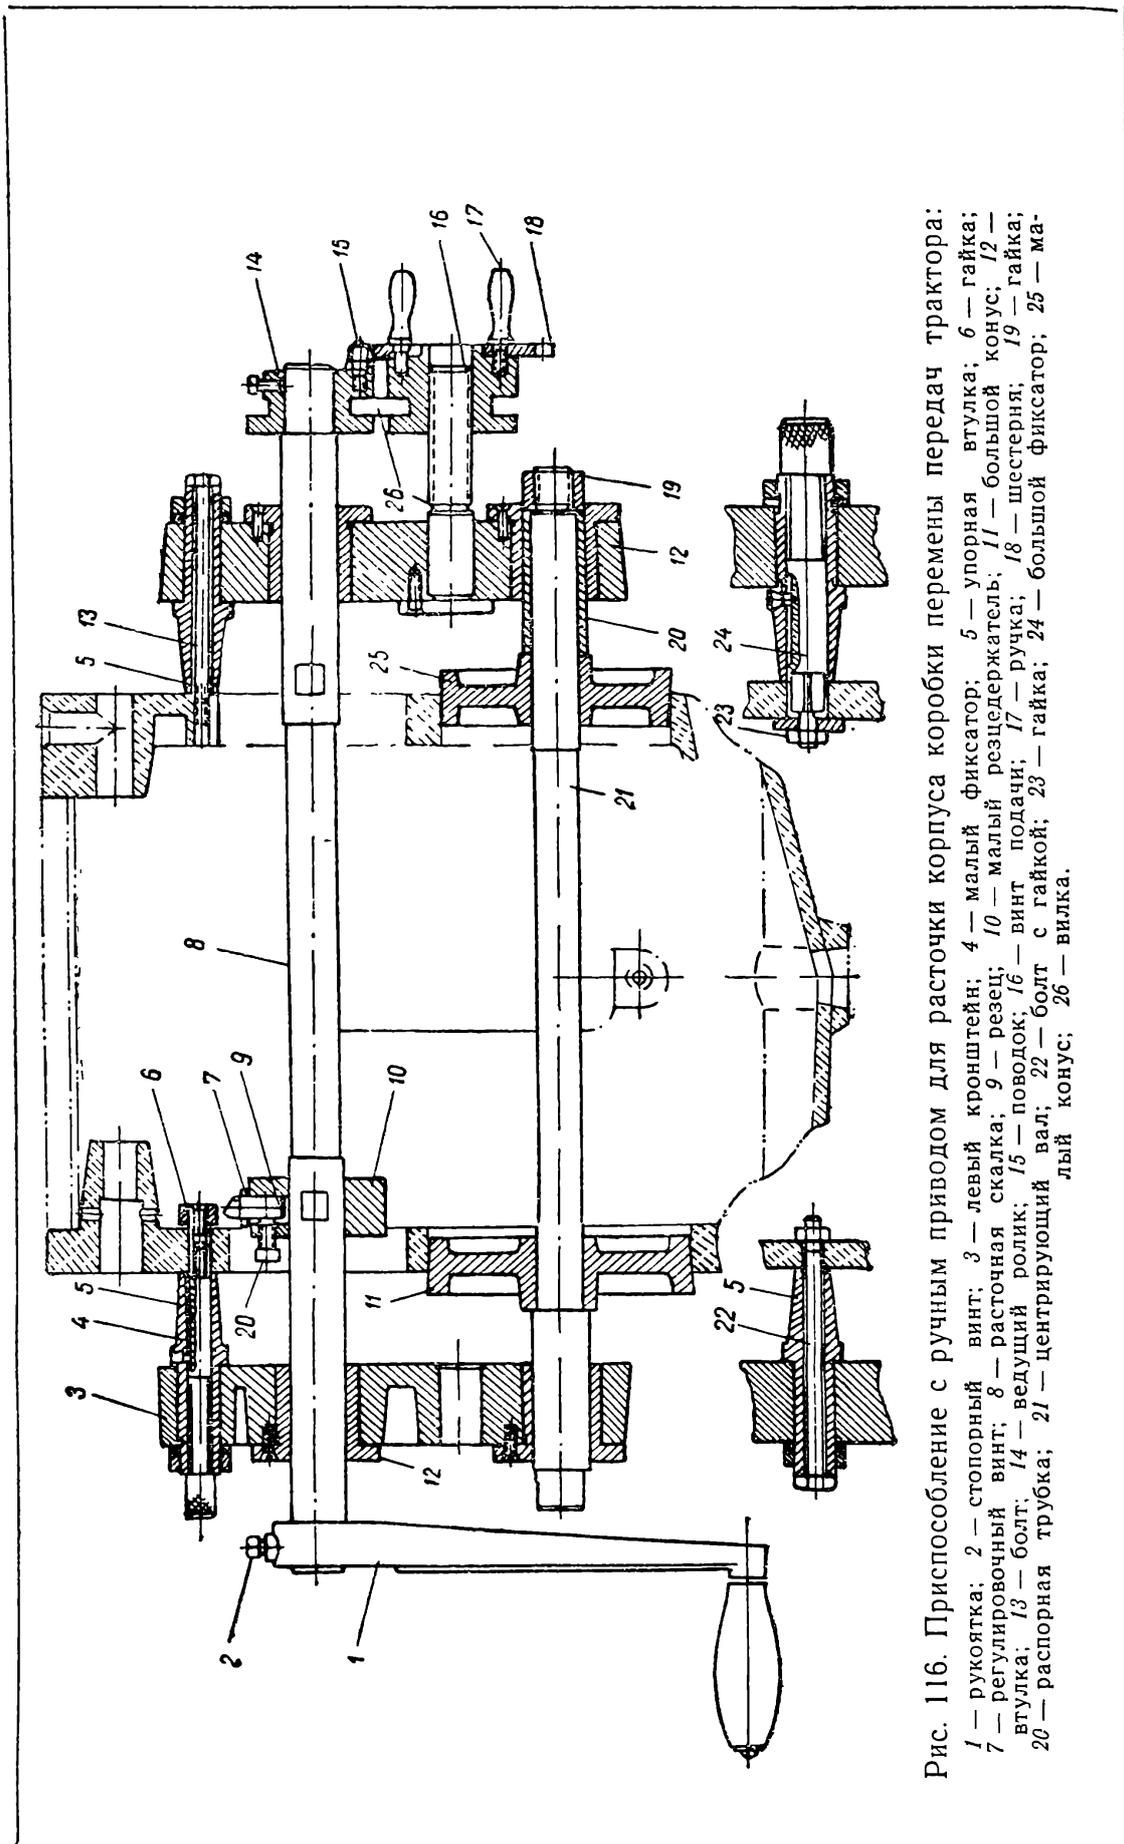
Приспособление с ручным приводом для расточки корпуса коробки перемены передач трактора:
